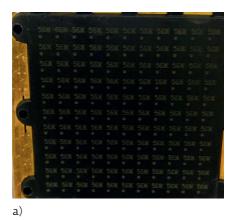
Загерметизированные пресс-материалом корпуса DFN
